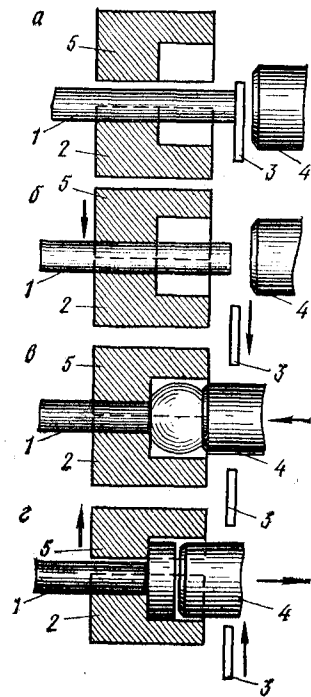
Схема штамповки изделия на горизонтально-ковочной машине
